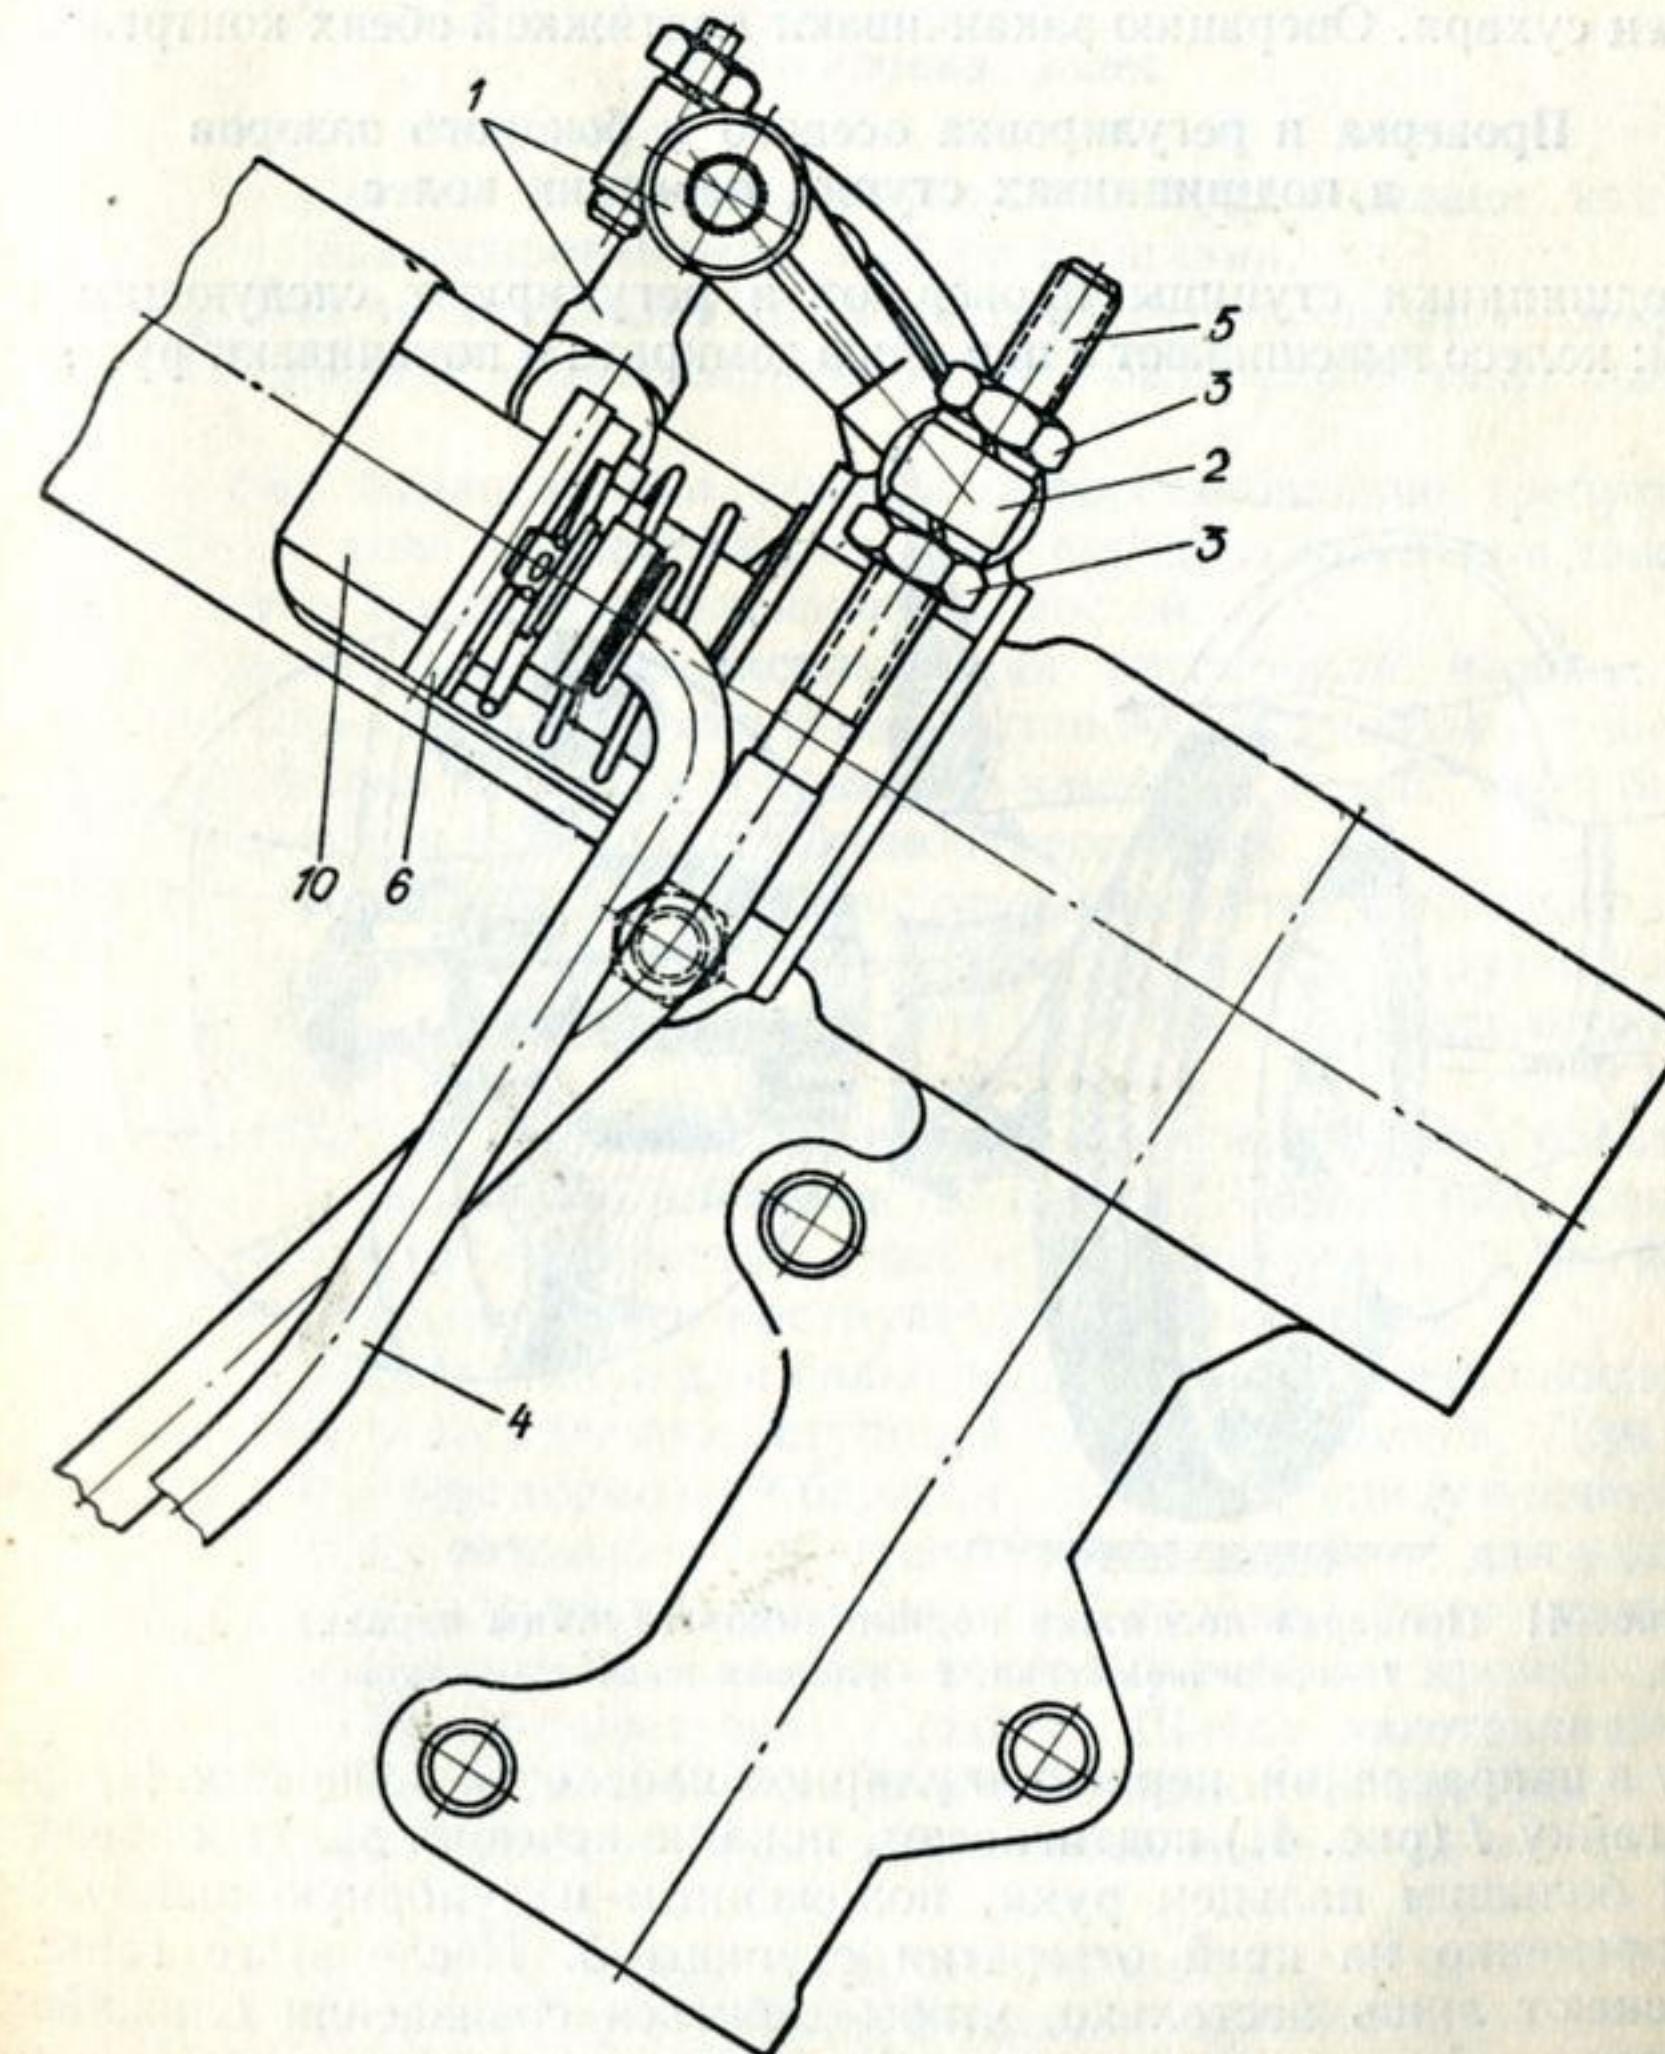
Регулировочный узел механизма привода управления коробкой передач (обозначения позиций см. рис. 28)
